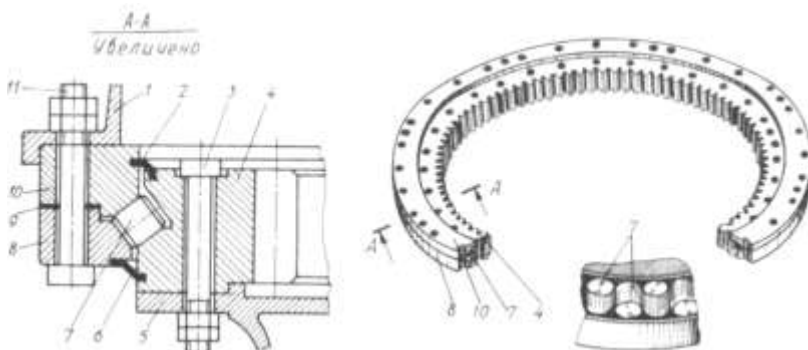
Опорно-поворотное устройство экскаватора ЭО-4112А
